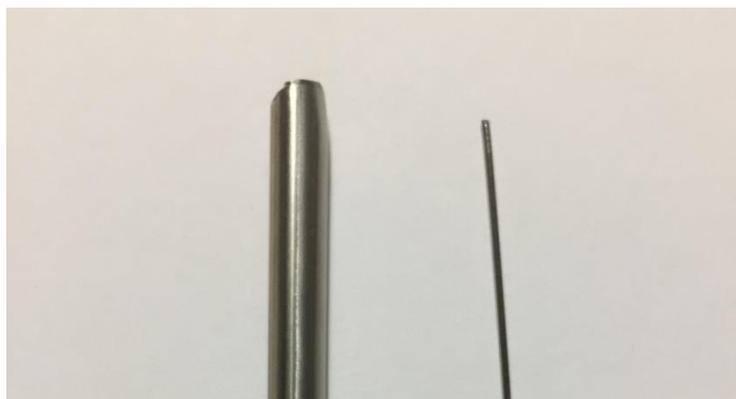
Diferença no diâmetro entre o tubo soldado e o trefilado
